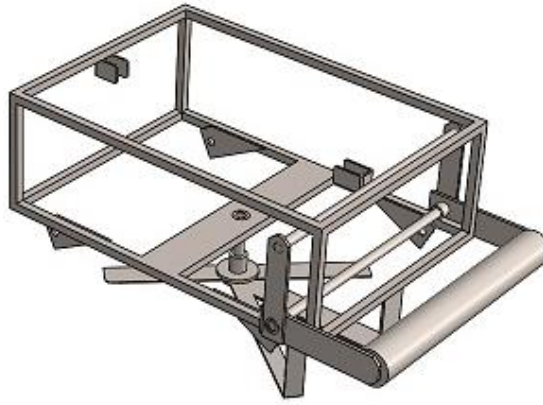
2: Montaje de soportes y sistema del rodillo al chasis
